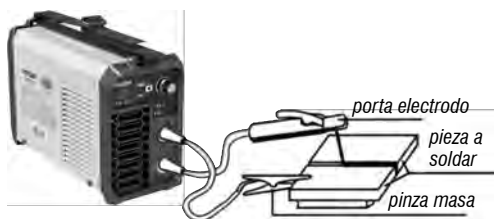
Montaje de los cables de soldadura para soldar electrodos recubiertos (MMA)
